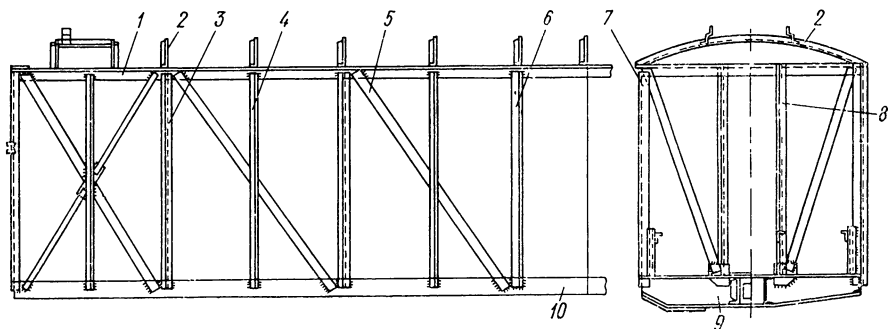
Металлический каркас вагона-ледника постройки 1937 г. с деревянной обшивкой
